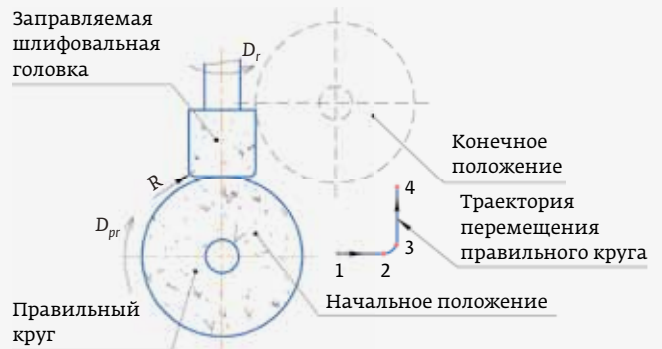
Схема правки шлифовальной головки (вид сверху)
